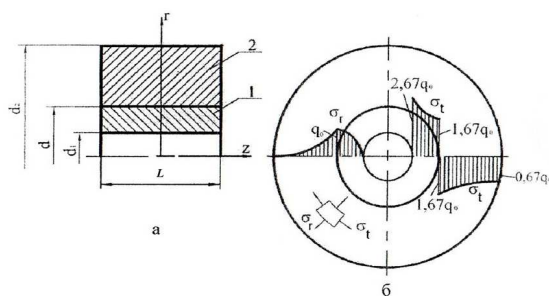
Гладкое цилиндрическое соединение с натягом: а – конструктивная схема; б – графики распределения напряжений в деталях соединения; 1 – охватываемая деталь (вал); 2 – охватывающая деталь
